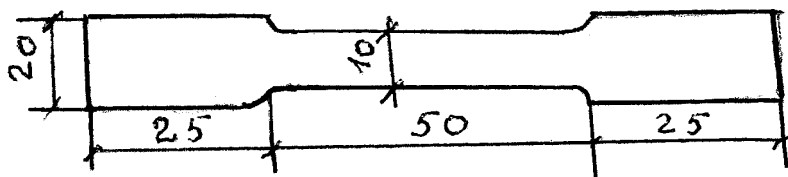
Размеры и форма образца пленки для определения разрывного удлинения
